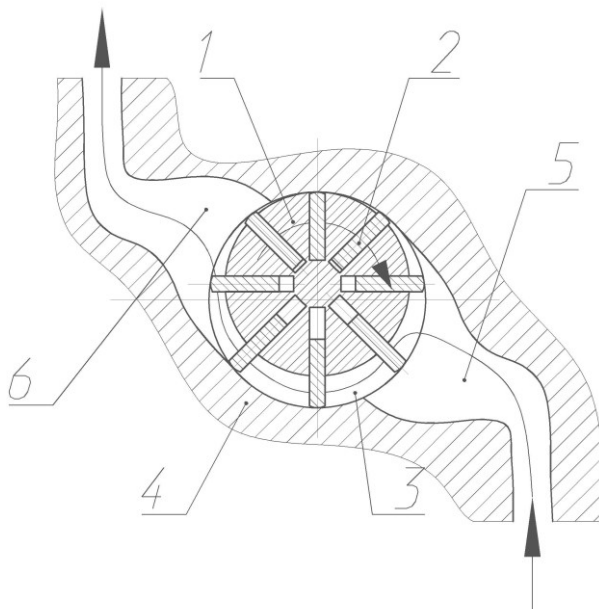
Схема шиберного насоса: 1-ротор; 2 - шиберы; 3 - объем между шиберами; 4 - корпус
